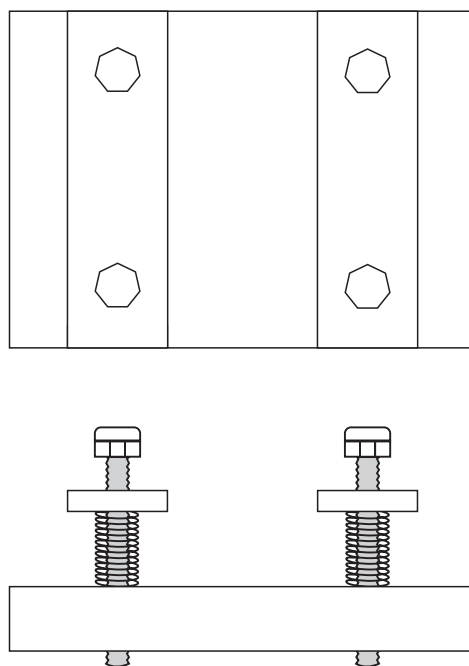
Dispositif de serrage pour les lanières (vues de dessus et latérale)
